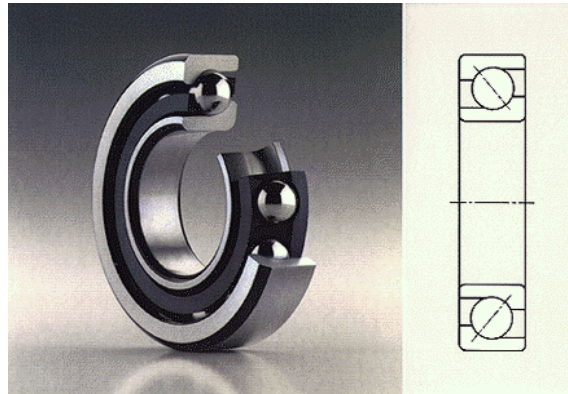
Rodamiento de bolas de contacto angular de una sola hilera.
